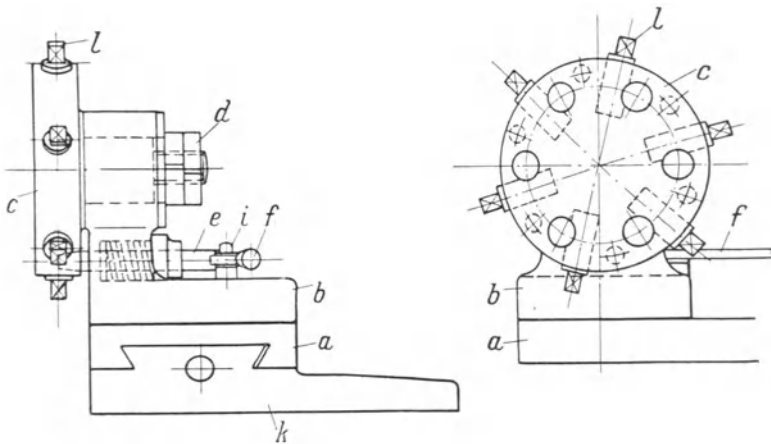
Vertikaler Revolverkopf für 6 Werkzeuge.
